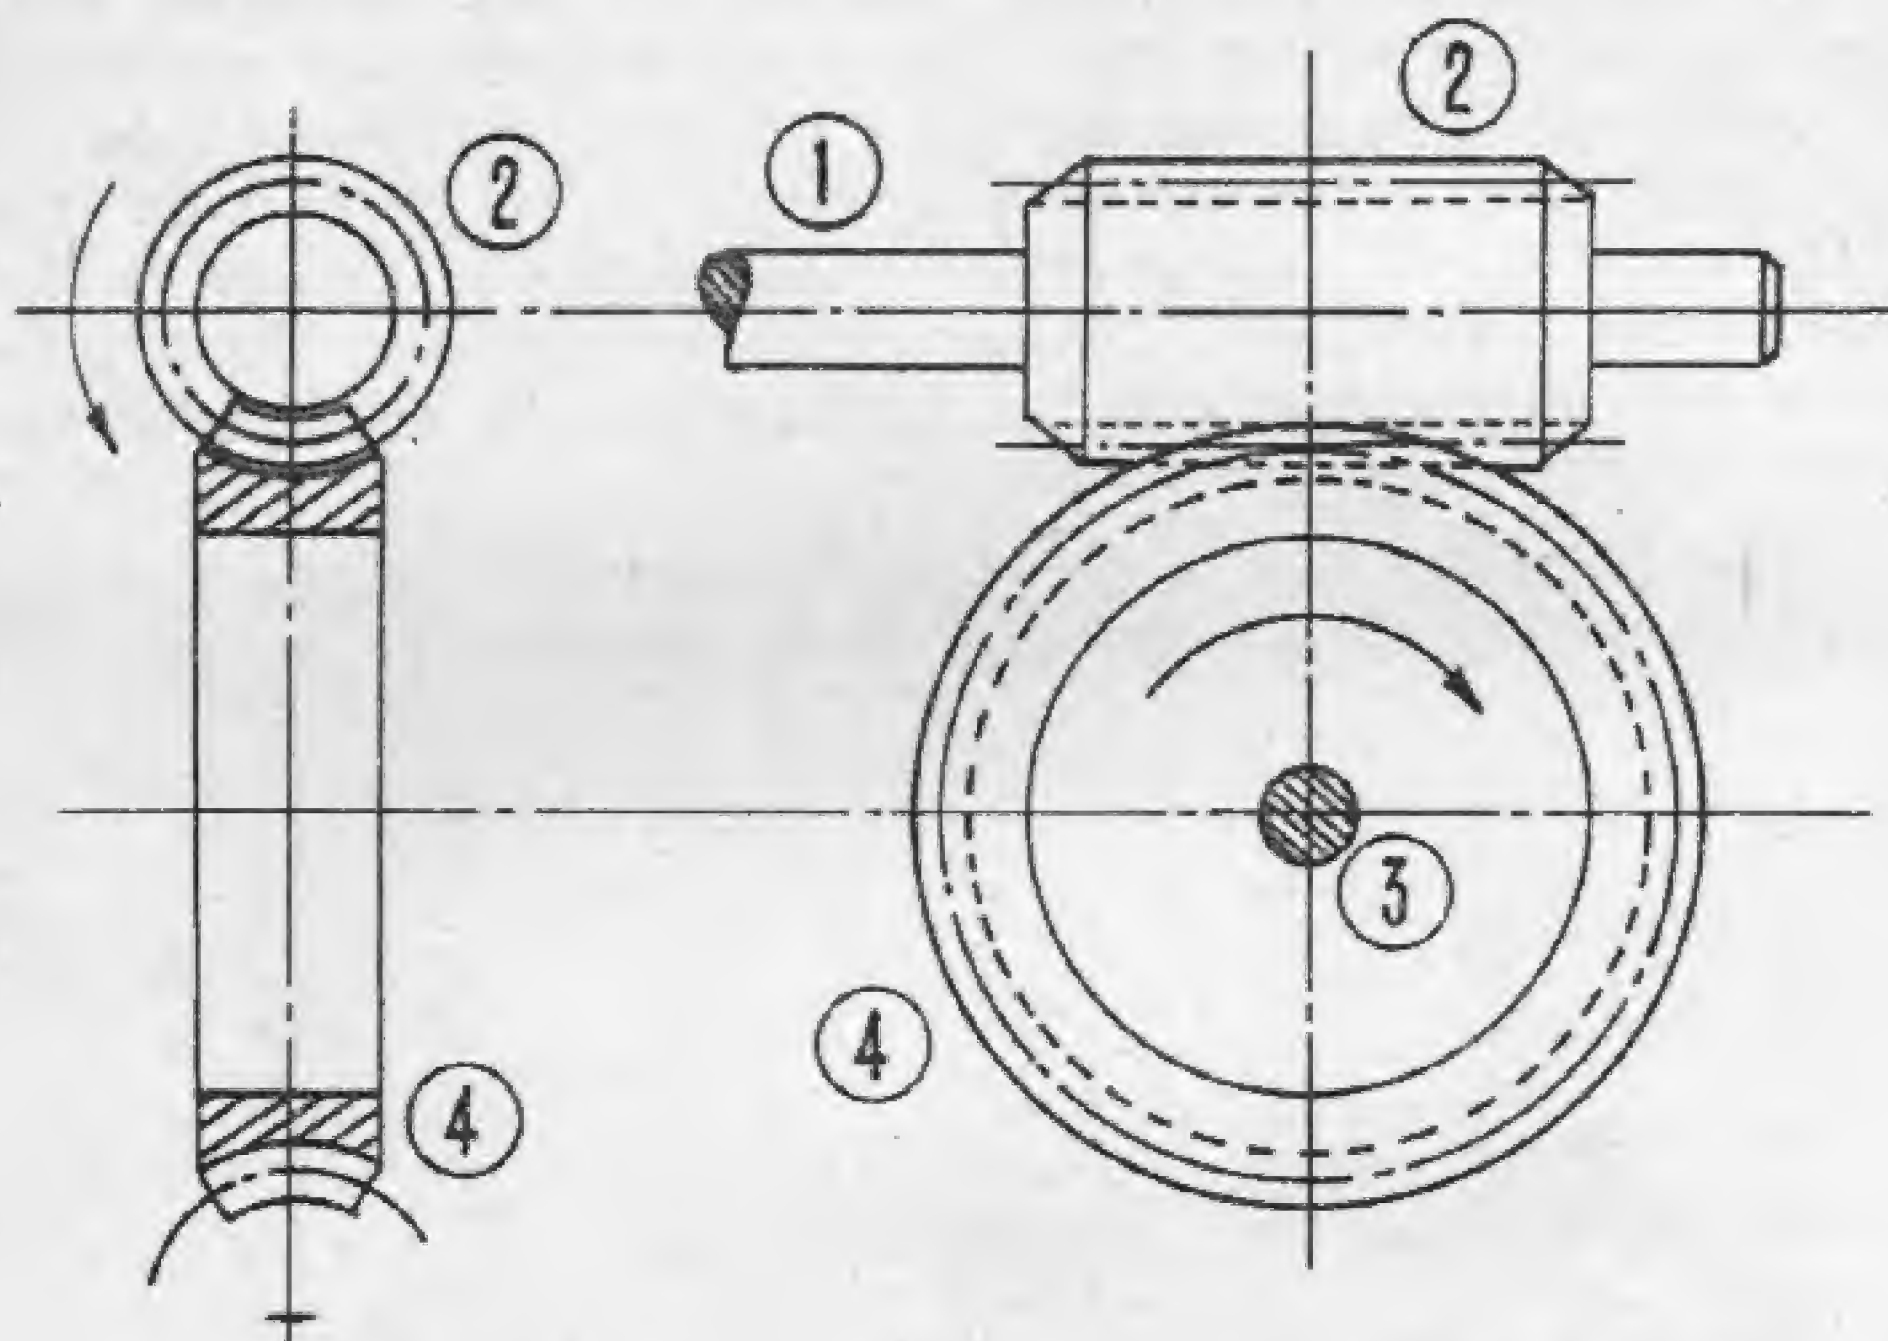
Tornillo sinfín colocado en el extremo del árbol de transmisión. (1) Árbol de transmisión; (2) vis sinfín; (3) eje de la corona; (4) corona.
